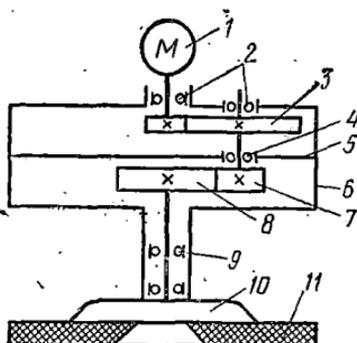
Кинематическая схема штукатурно-затирочной машины СО-112:
